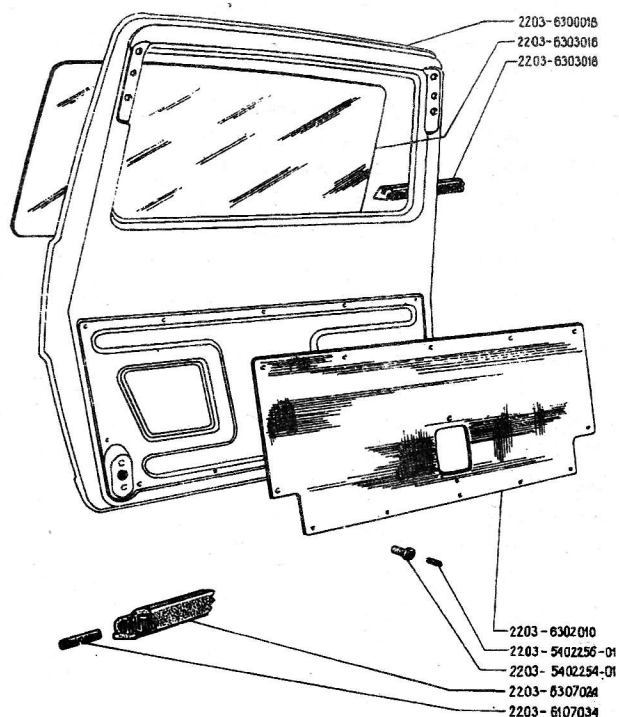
Дверь задняя в сборе; обивка; окно; уплотнители
